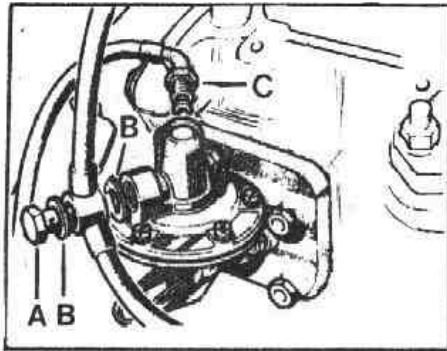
Desmontaje tuberías bomba - de combustible
